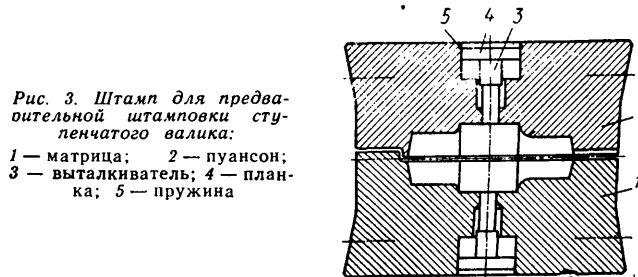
Штамп для предварительной штамповки ступенчатого валика:
